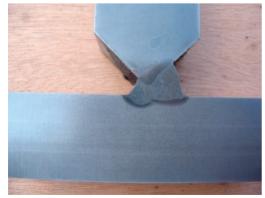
組立溶接試験 (ルート間隔 2.5mm)
